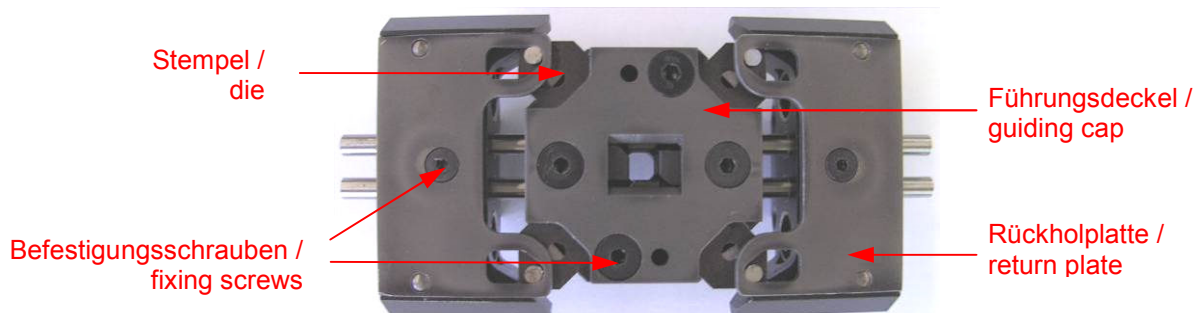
Crimpwerkzeug / Crimping tool
